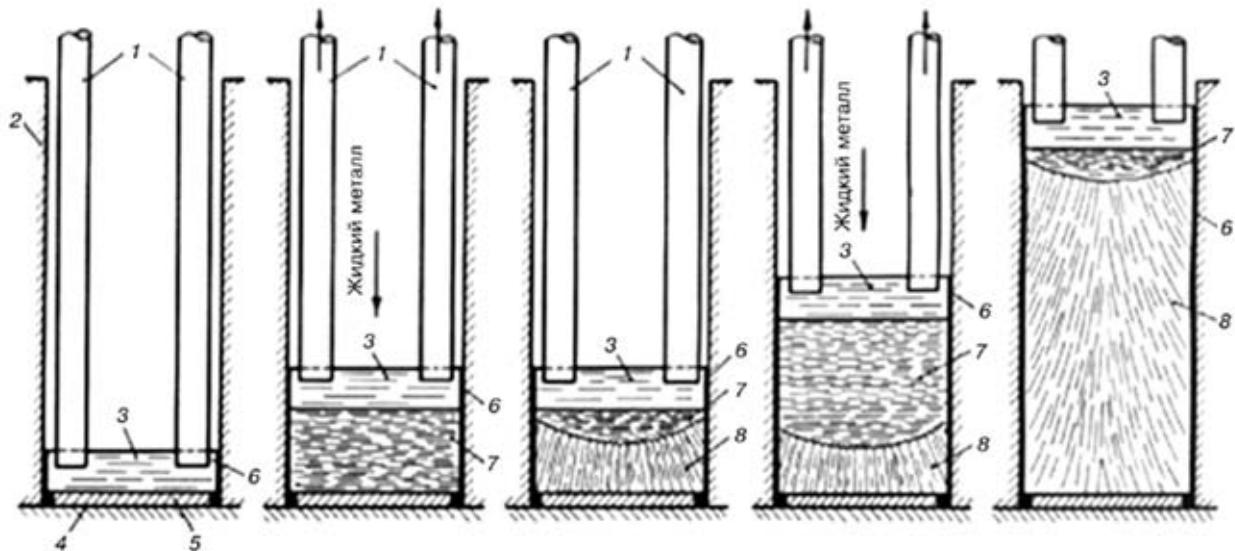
Схема порционной электрошлаковой отливки: 1 — нерасходуемые электроды; 2 — кристаллизатор; 3 — шлаковая ванна; 4 — поддон; 5 — затравка; 6 — гарнисаж; 7 — металлическая ванна; 8 — твердый металл
